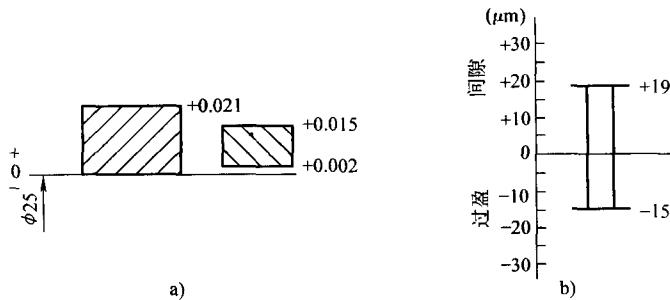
4 例 1—1 的尺寸公差带图和配合公差带图
